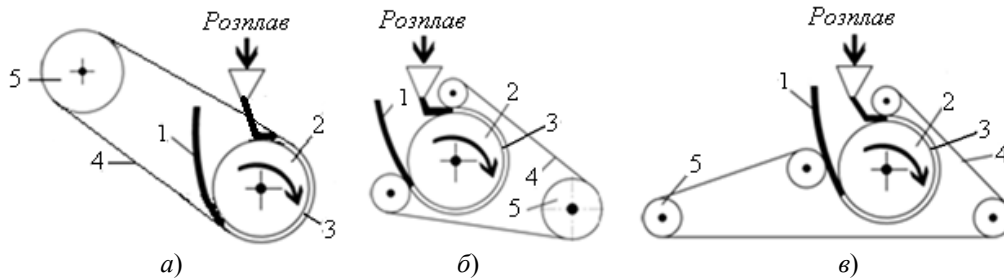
Схеми охоплення ливарного колеса сталевією стрічкою:
